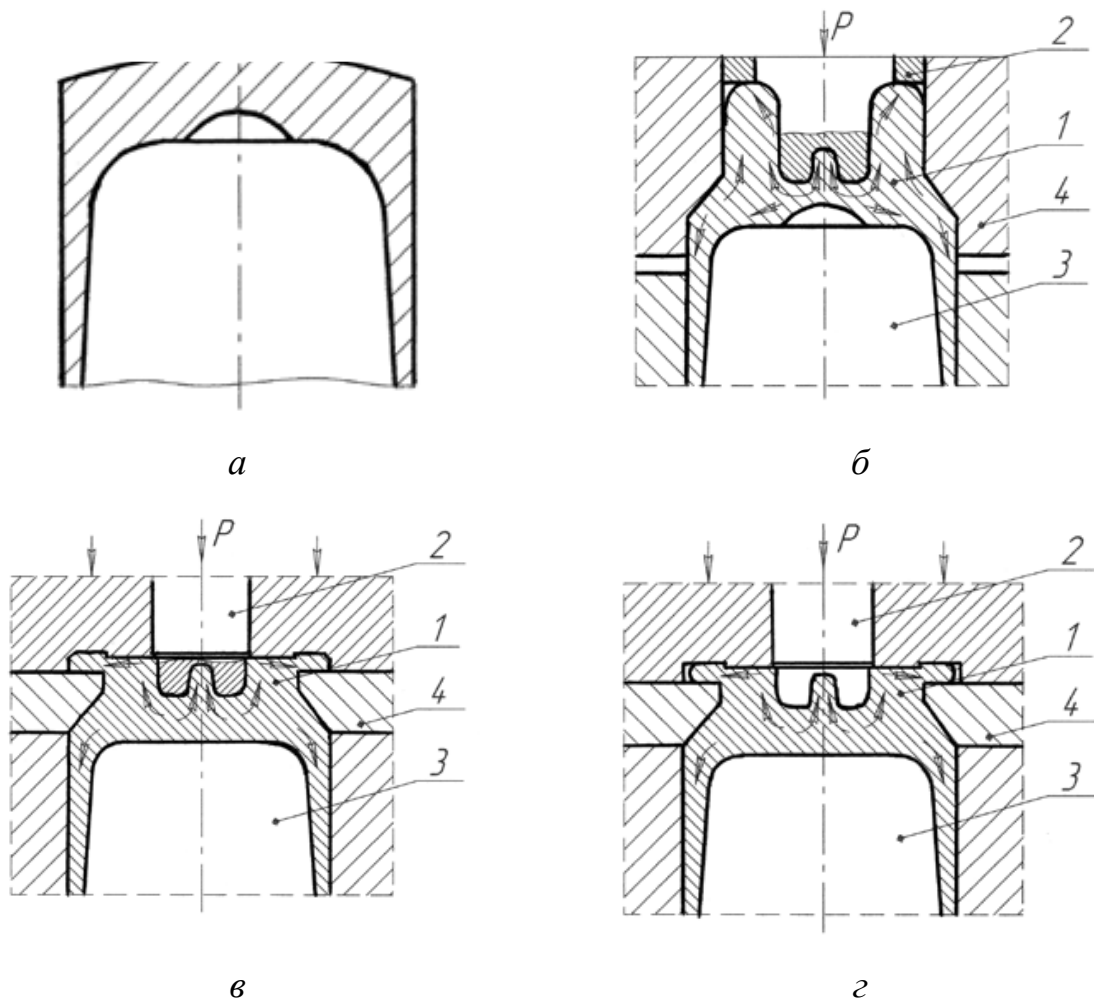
Технологічні схеми двоопераційного точного штампування дна гільз: а - вихідна заготовка; б - перше штампування; в - друге штампування з калібруванням фланця; г - друге штампування без калібрування фланця; 1 – заготовка; 2 – ступінчастий пуансон; 3 – опорний пуансон; 4 - матриця
